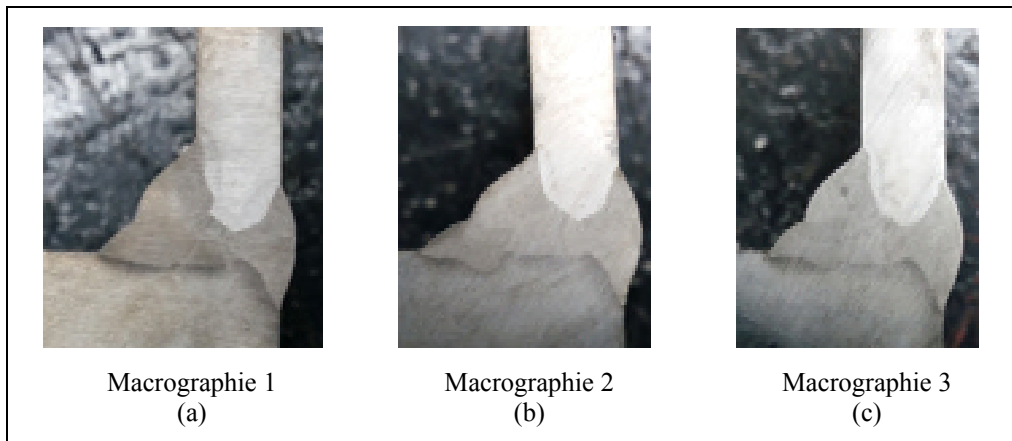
Macrographies du modèle de joint soudé
